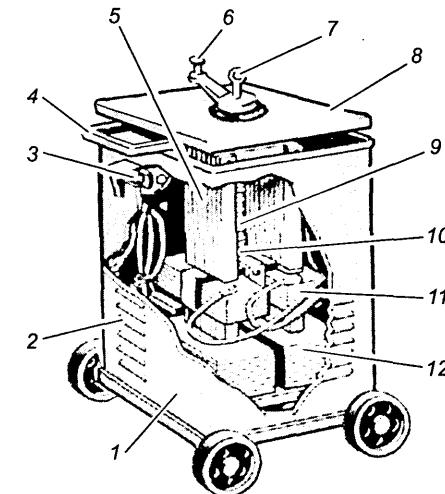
Основные части сварочного трансформатора:
